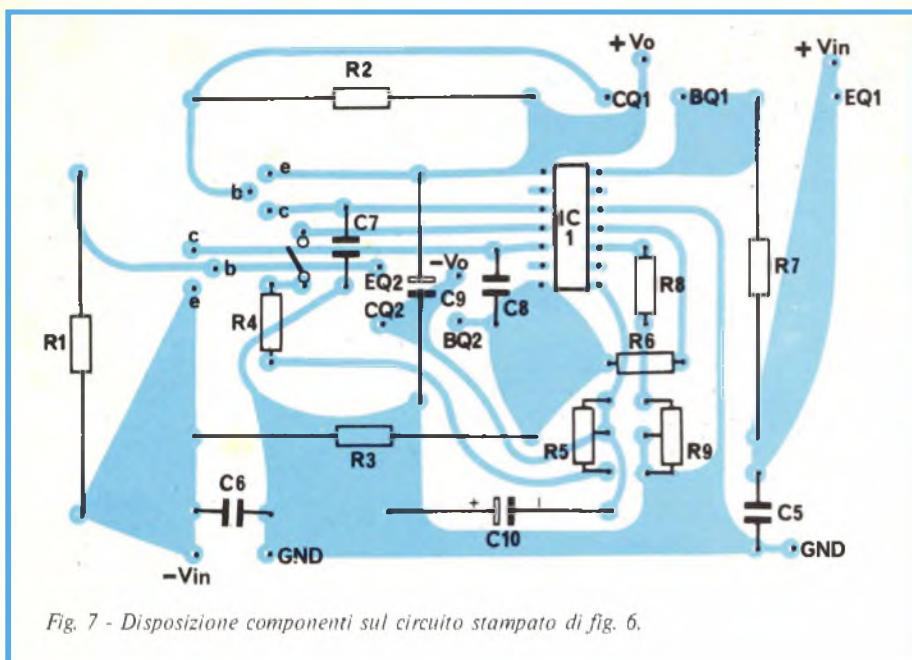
Disposizione componenti sul circuito stampato di fig. 6.
